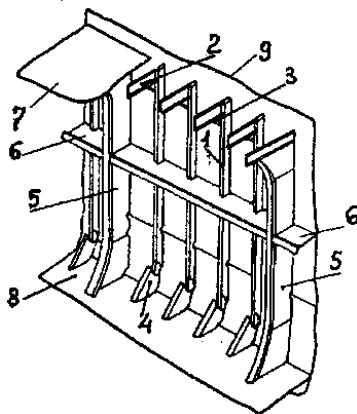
Конструкция бортового перекрытия при поперечной системе набора: 1 - шпангоут; 2 - бимс; 3 - бимсовая кница; 4 - скуловая кница; 5 - рамный шпангоут; 6 - бортовой стрингер; 7 - настил палубы; 8 - настил второго дна; 9 - обшивка борта
